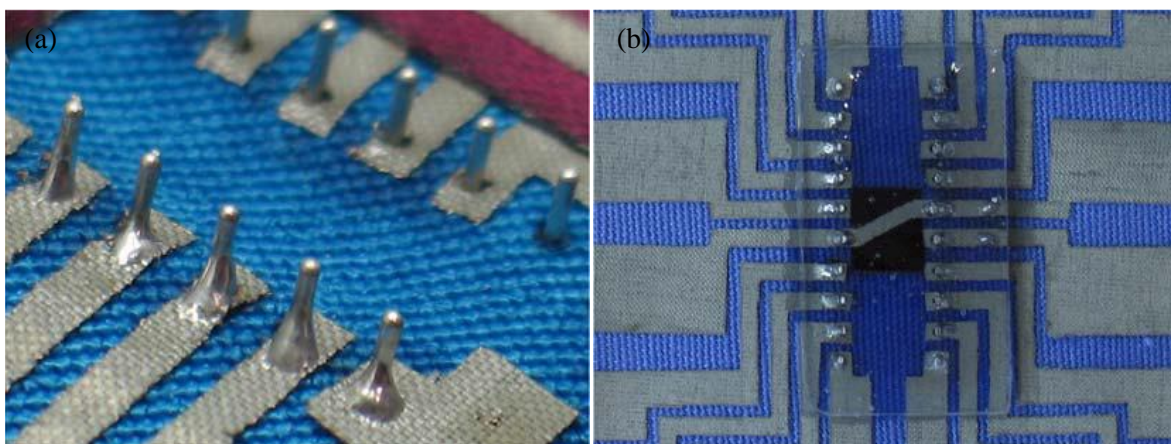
(a) Connection par soudure entre un tissu et un PCB et (b) connexion par soudure encapsulée dans de l'époxy [46]
